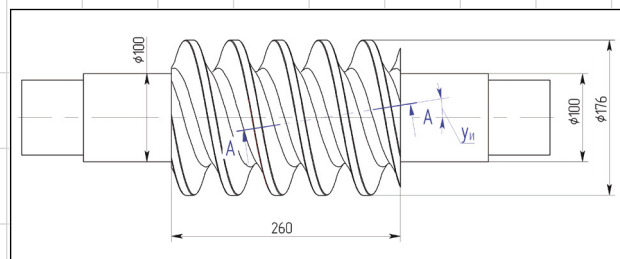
Схема червяка, образованного тором (форма профиля ZT2)
